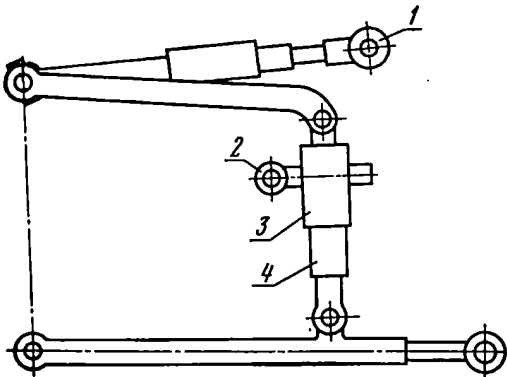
Схема навесной системы трактора К-700, подготовленной для агрегатирования с плугом ПН-8-35
